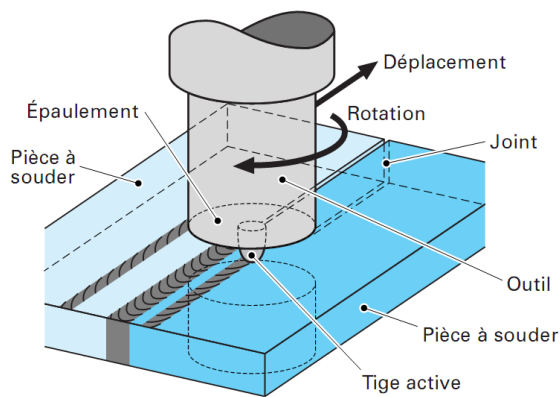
Schéma de principe du soudage par friction-malaxage (FSW) [40].
